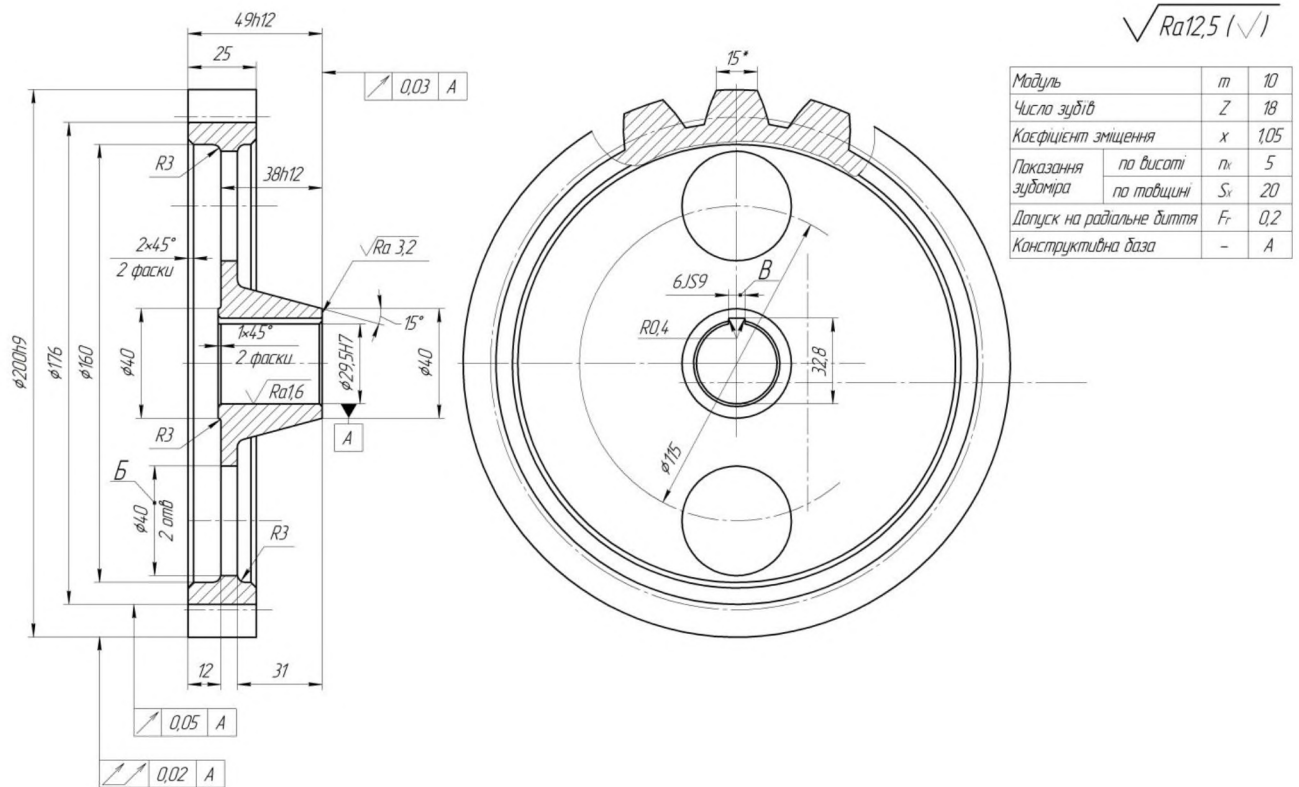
Креслення деталі «Колесо зубчасте»
